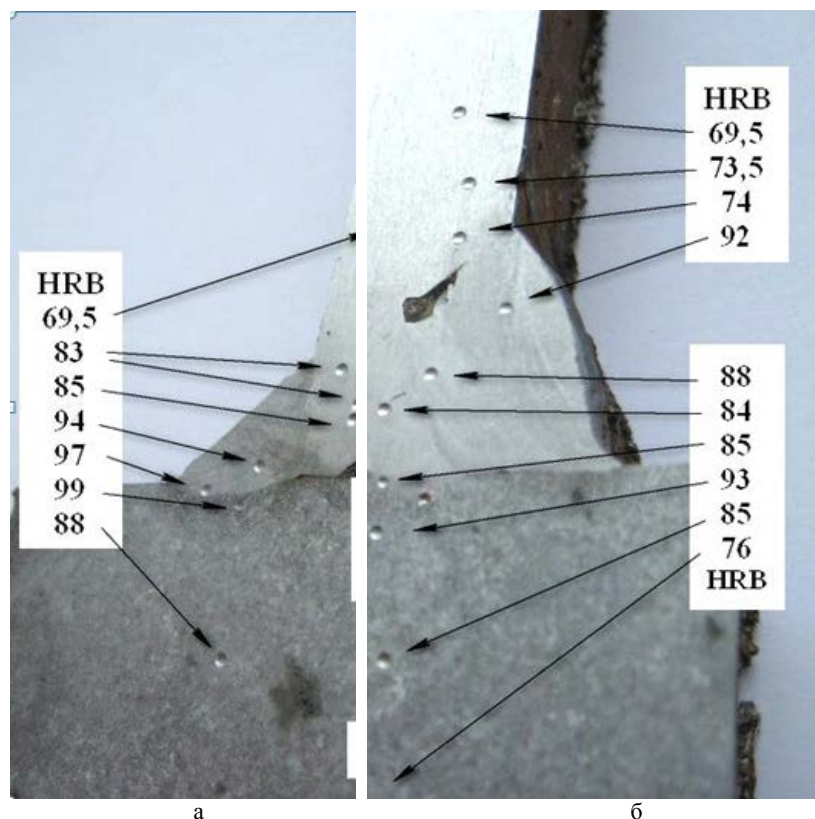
Распределение твердости в лито-сварном соединении (ребро жесткости из стали 09Г2С на основном металле литой заготовки из стали 35Л) при различных режимах сварки: а – режим 1, б – режим 2
